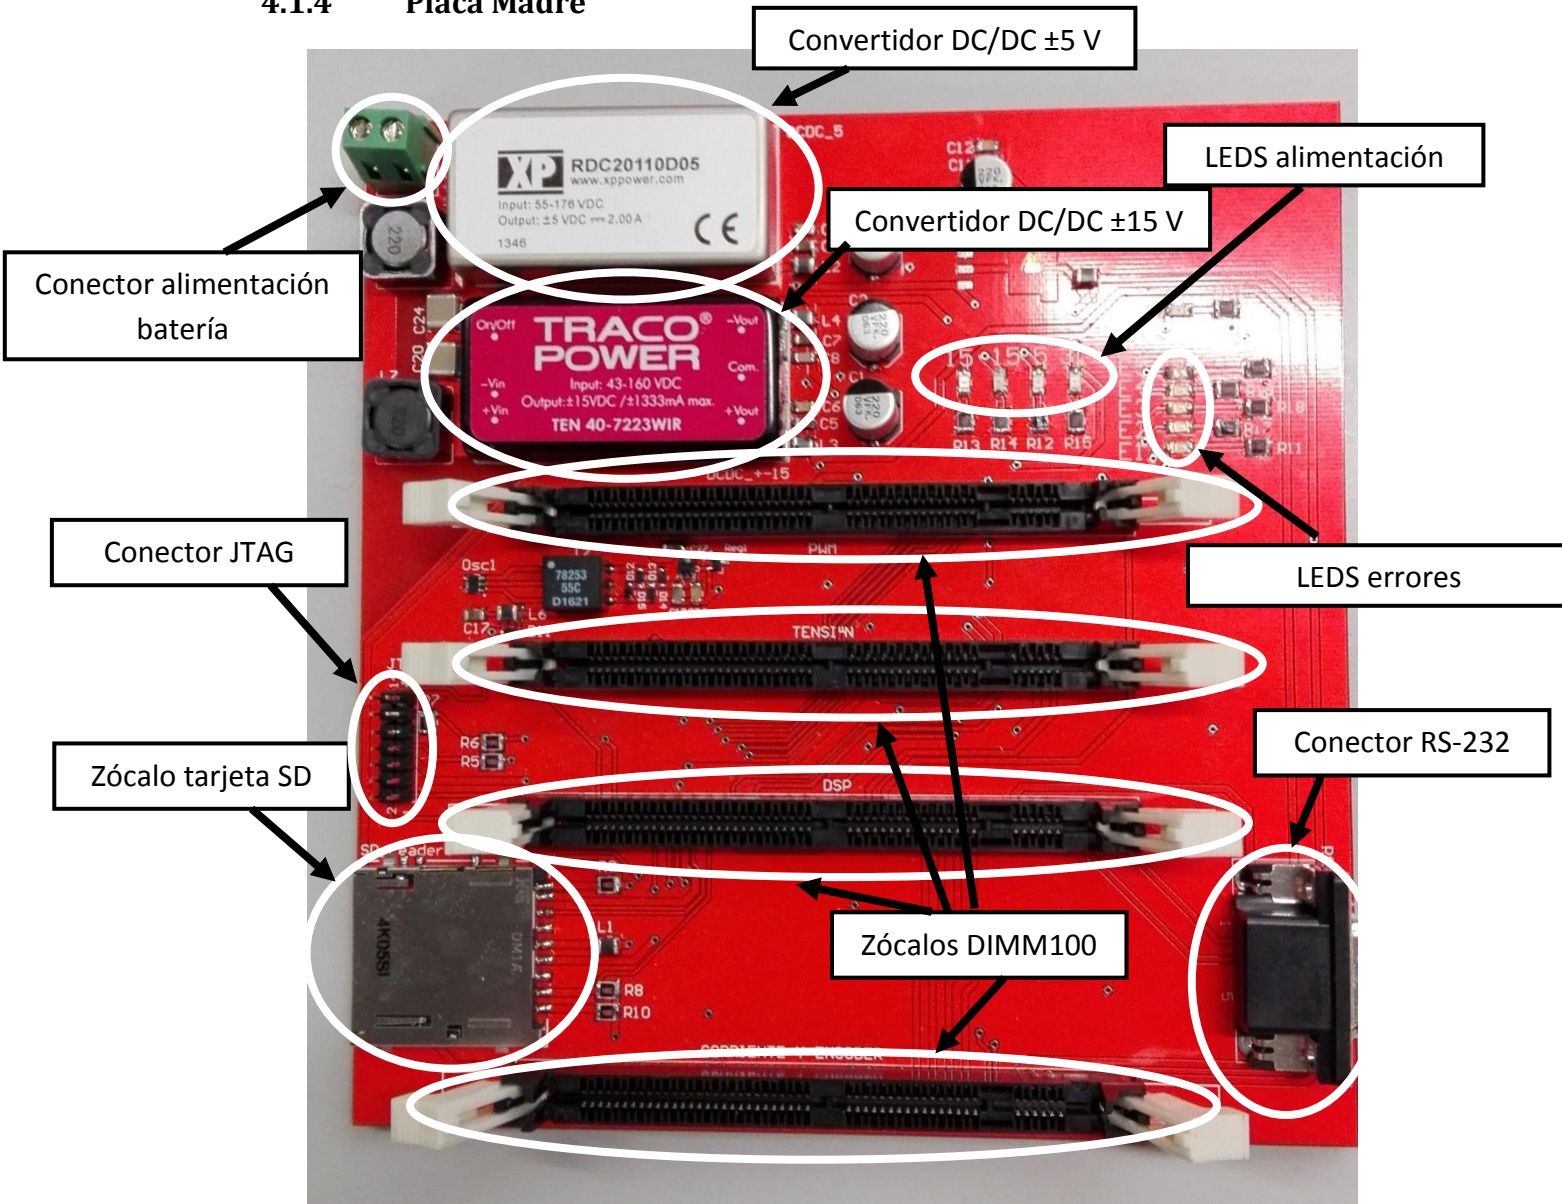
Fotografía de la parte 'Top' de la placa madre
